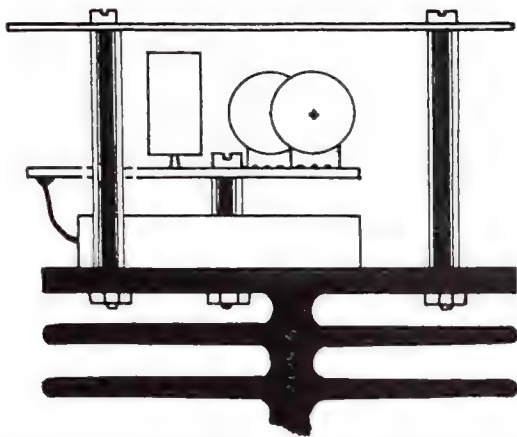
Ansicht von oben. Sie zeigt deutlich, wie die Mechanik „zusammenhängt“.
